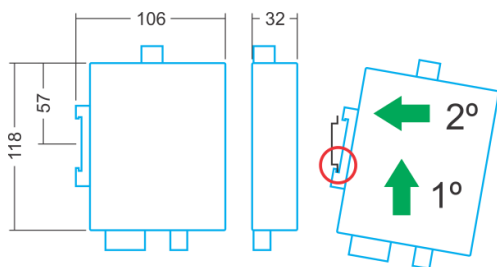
Dimensões e montagem do Transmissor de Pesagem Automática 2711
